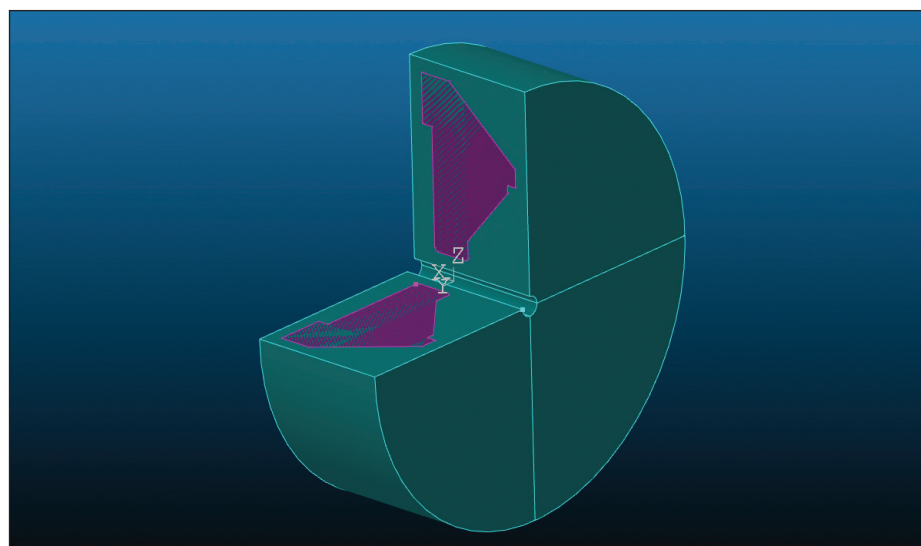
Заготовка для токарной обработки, построенная по сечению модели
